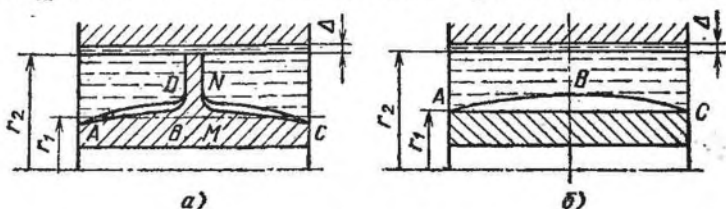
Поперечное сечение рабочей ячейки в области минимального зазора между колесом и корпусом:
